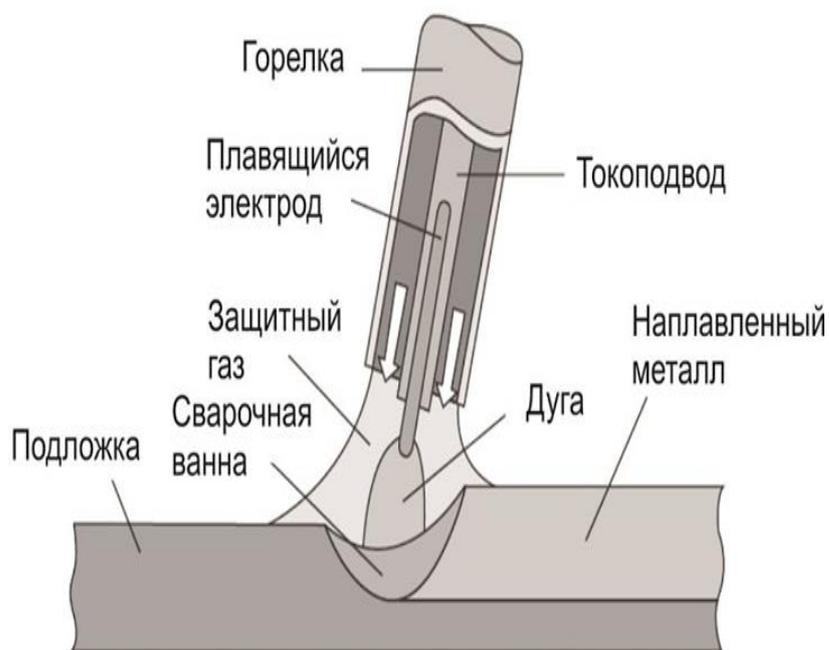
Эскиз процесса механизированной сварки в защитных газах
